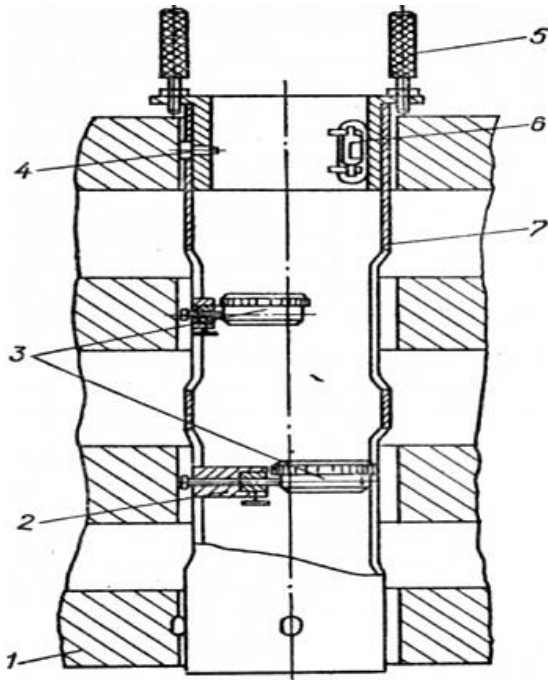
Пристрій для контролю взаємного зміщення опор блок-картра під колінчастий вал двигуна.
